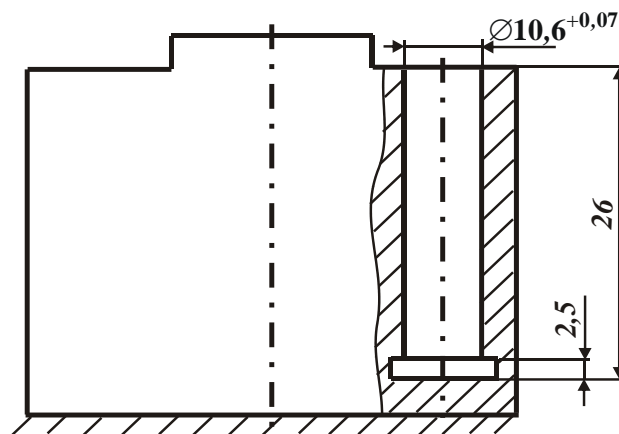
Схема розташування глухого отвору у агрегаті "блок циліндрів"
